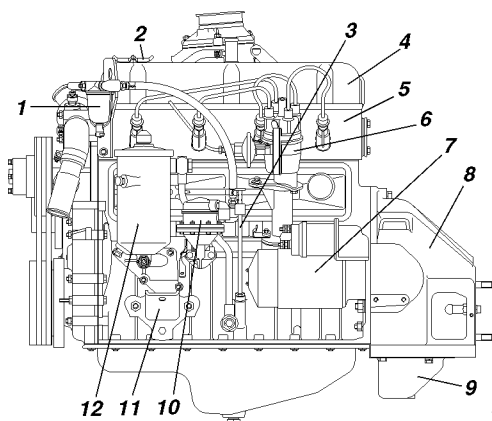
Двигатели ЗМЗ (вид слева):
